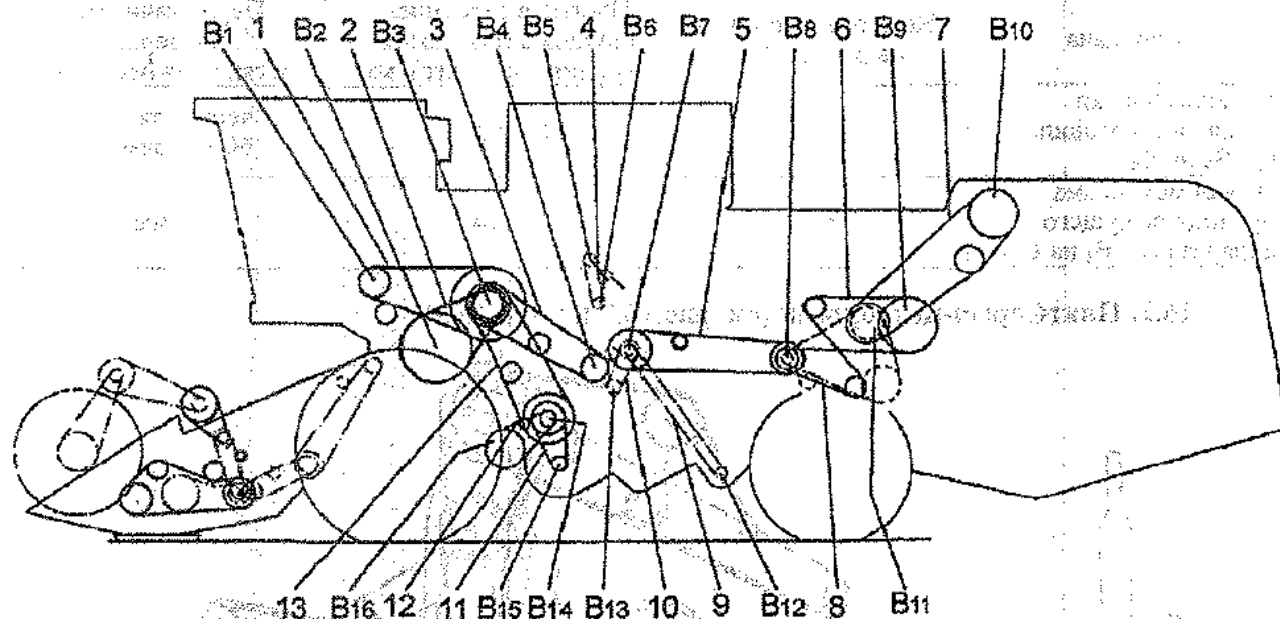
Схема ремённых и цепных передач комбайнов «Дон» (левая сторона): 1-передача на вал битера; 2-передача на вал барабана; 3-передача на вал домолачивающего устройства; 4-передача на вал наклонного выгрузного шнека; 5-передача на вал колосового элеватора; 6-передача на вал соломотряса; 7-передача на вал соломонабивателя; 8-передача на вал половонабивателя и контрпривода соломонабивателя; 9-передача на нижний вал колосового элеватора; 10-передача на вал распределительного шнека; 11-вал контрпривода вентилятора очистки; 12-передача на вал вариатора вентилятора; 13-передача на колебательный вал очистки; В1-вал двигателя; В2-вал барабана; В3-вал битера; В4-вал домолачивающего устройства; В5-вал контрпривода наклонного выгрузного шнека; В6-вал наклонного выгрузного шнека; В7-вал верхний колосового элеватора; В8-вал заднего контрпривода; В9-вал соломотряса; В10-вал соломонабивателя; В11-вал половонабивателя; В12-вал нижнего колосового элеватора; В13-вал распределительного шнека; В14-вал контрпривода вентилятора очистки; В15-вал вариатора вентилятора; В16-вал колебательный очистки
